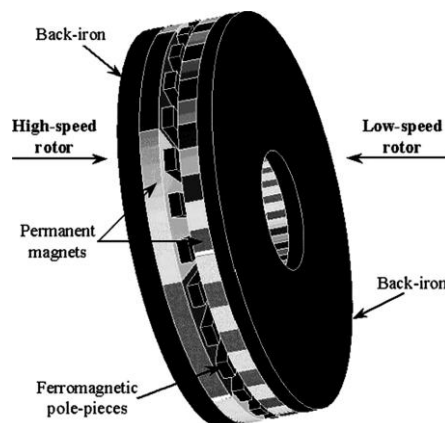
Engrenage magnétique à flux axial [MEZ06].
